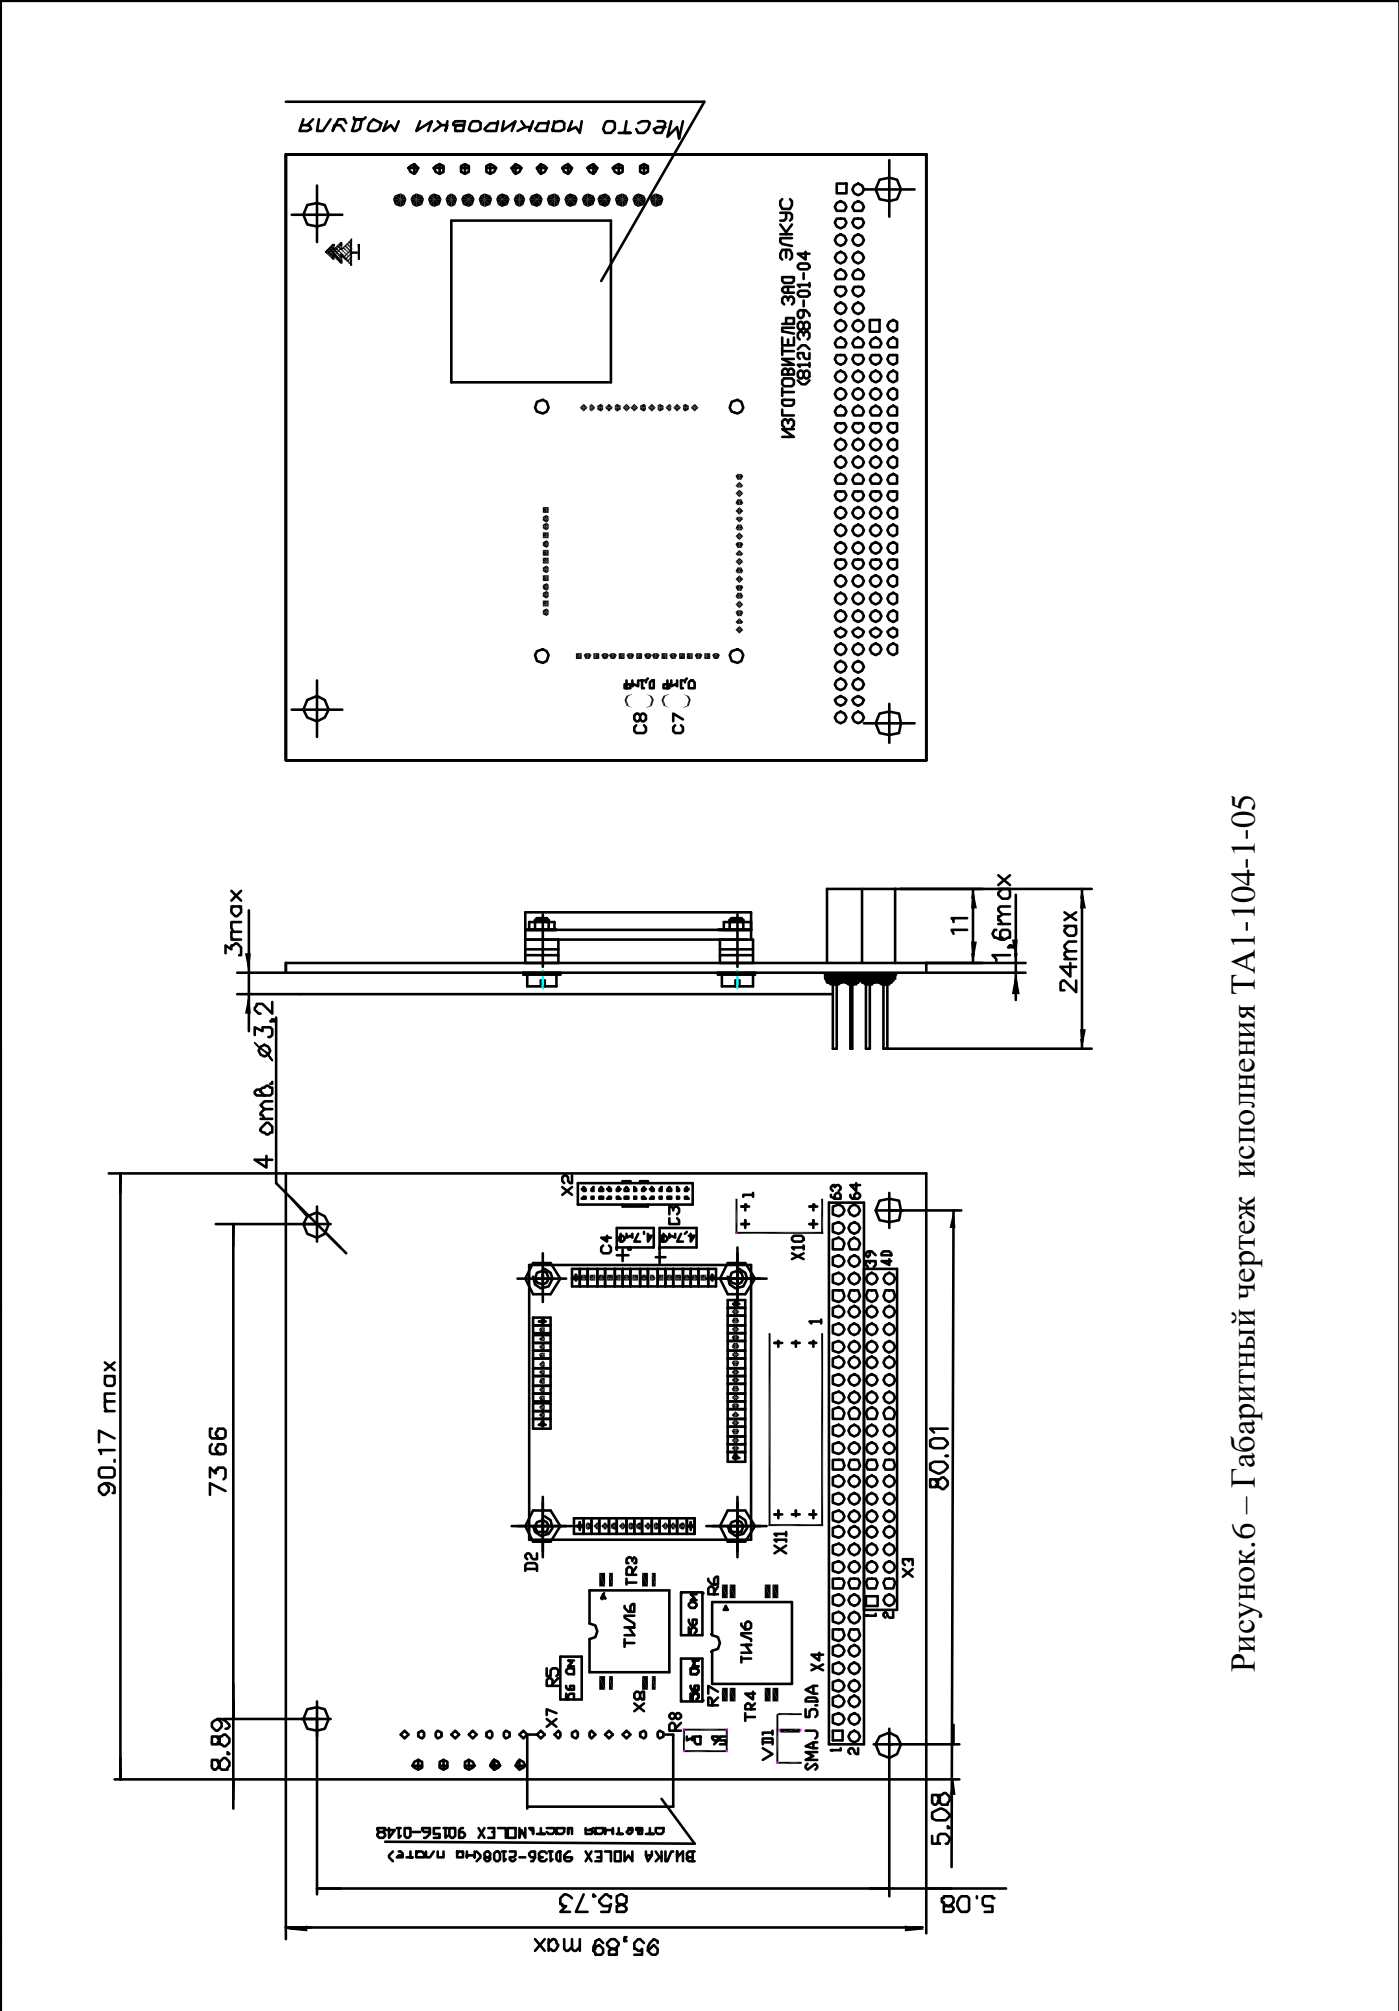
Габаритный чертеж исполнения ТА1-104-1-05
